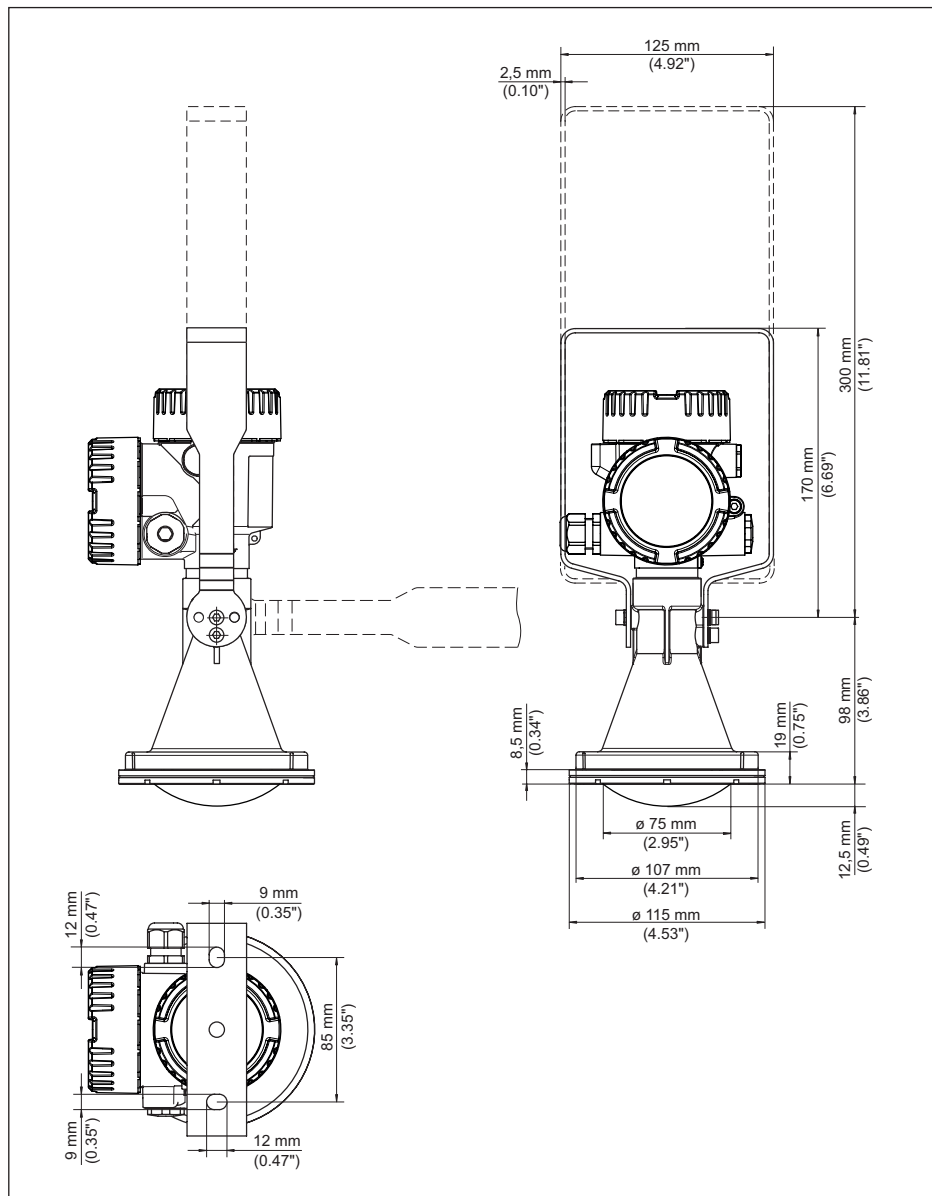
NCR-86, antena de plástico tipo corneta, suporte de montagem com 170 ou 300 mm de comprimento
